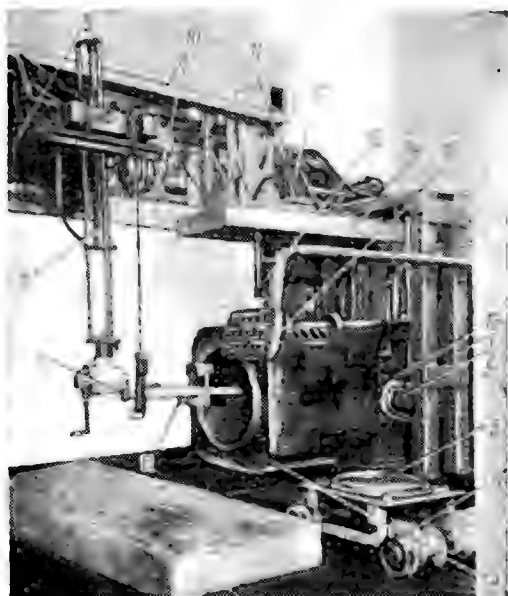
Общий вид рабочей позиции сборочного конвейера с комплексной механизацией монтажа магнитной системы остовов тяговых двигателей НБ-406 и НБ-411:
